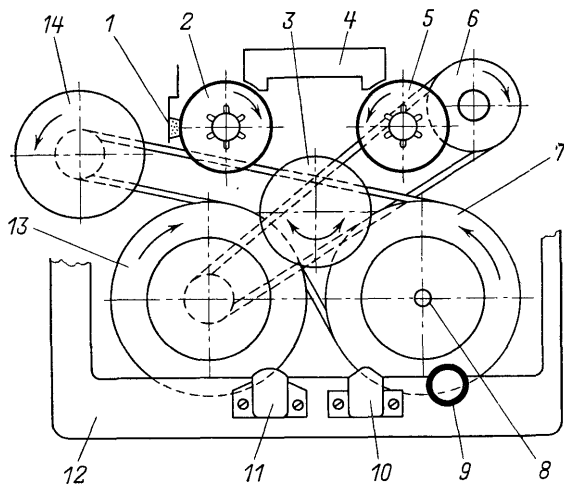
Кинематическая схема ЛПМ магнитофонов «Весна-305» и «Весна-306».
